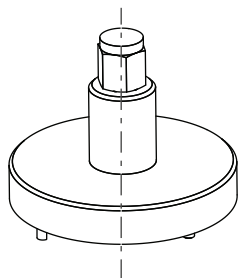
Clé PV M40 813 pour couvercle de carter de la pompe turbomoléculaire
